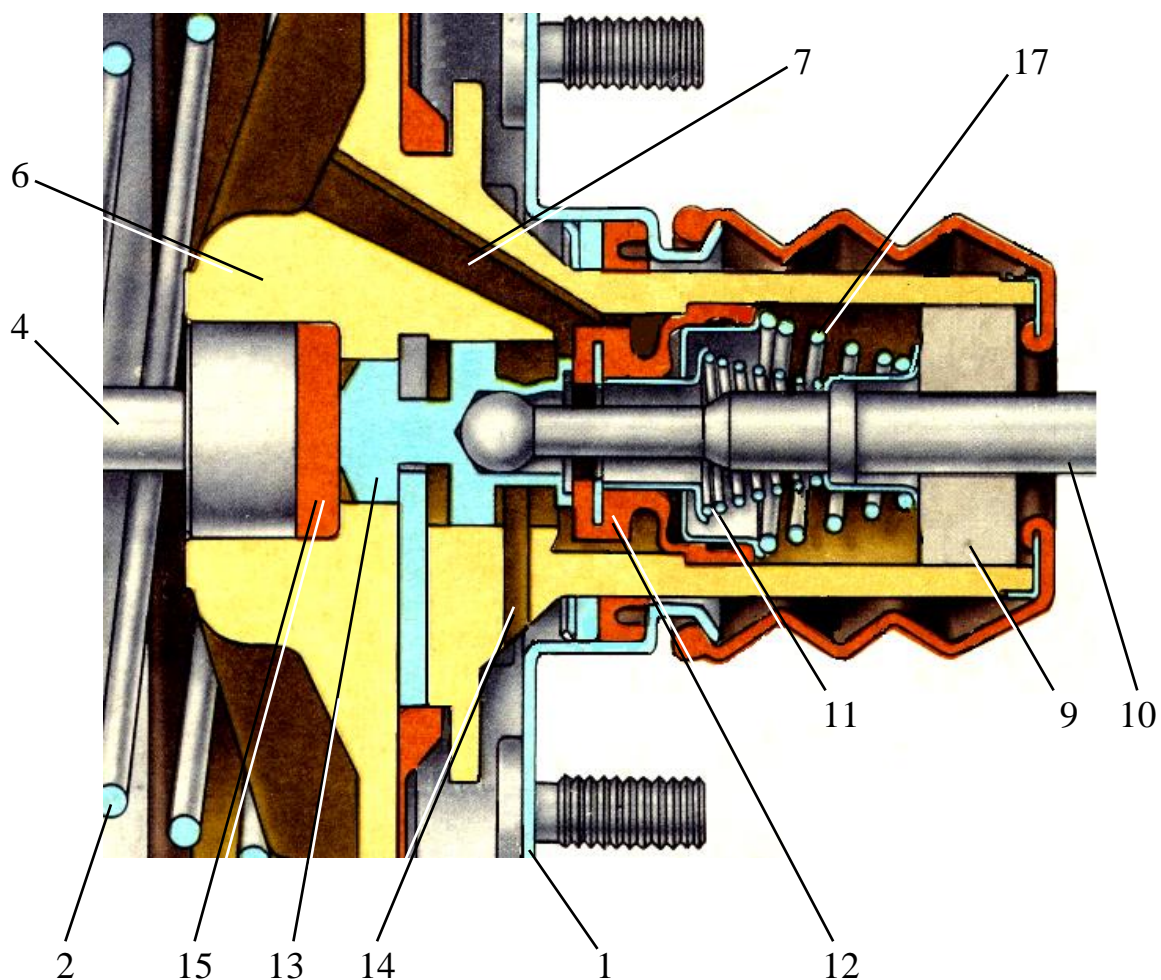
Конструкция клапанов вакуумного усилителя гидравлического тормозного привода: 1 – корпус усилителя; 2 – пружина; 4 – шток; 6 – поршень усилителя; 7 и 14 – каналы; 9 – фильтр; 10 – шток педали; 11 – пружина вакуумного клапана; 12 – вакуумный клапан; 13 – плунжер; 15 – упругая шайба; 17 – возвратная пружина вакуумного клапана
